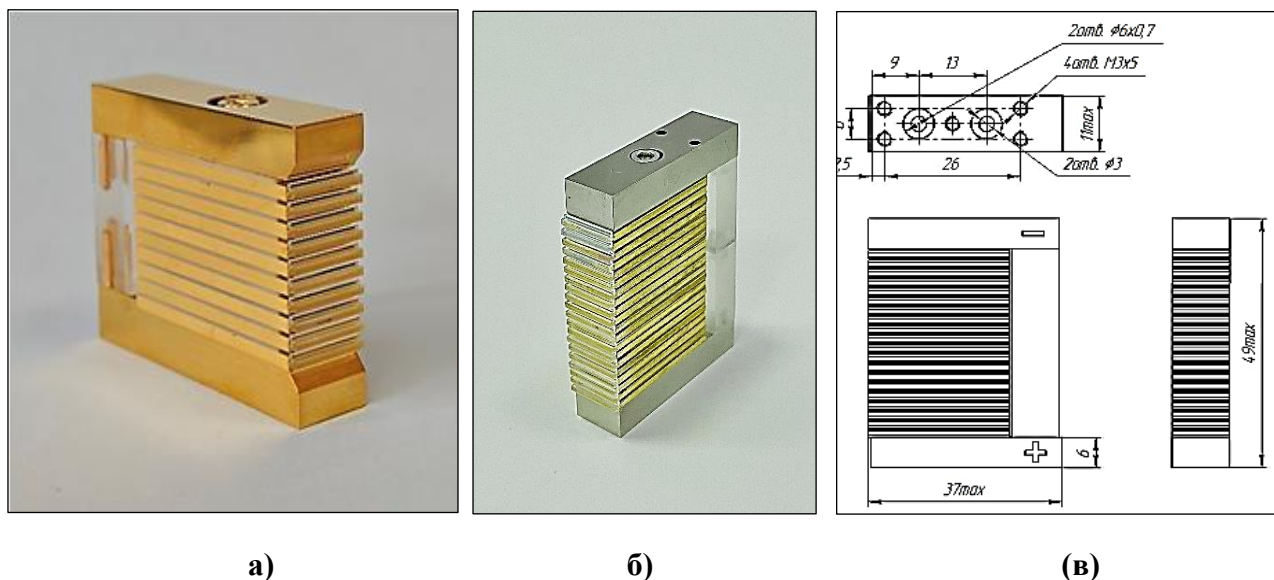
Внешний вид (а,б) и габаритный чертеж лазерного модуля (в).
